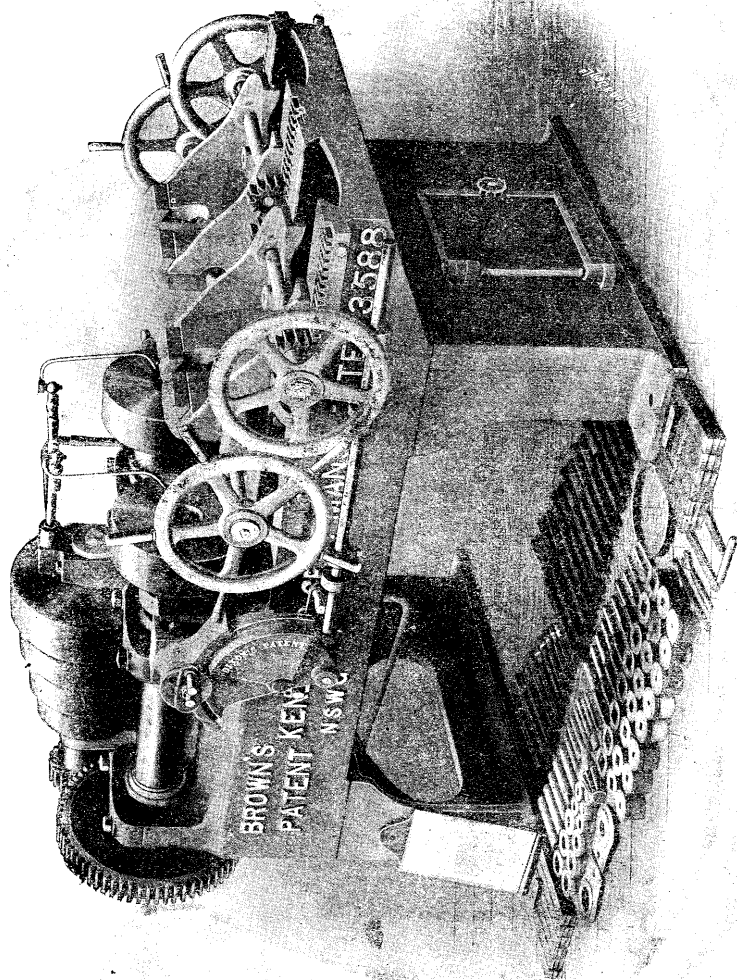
Taraudeuse double, construite par M. M. Kendall et Gent, de Manchester.
